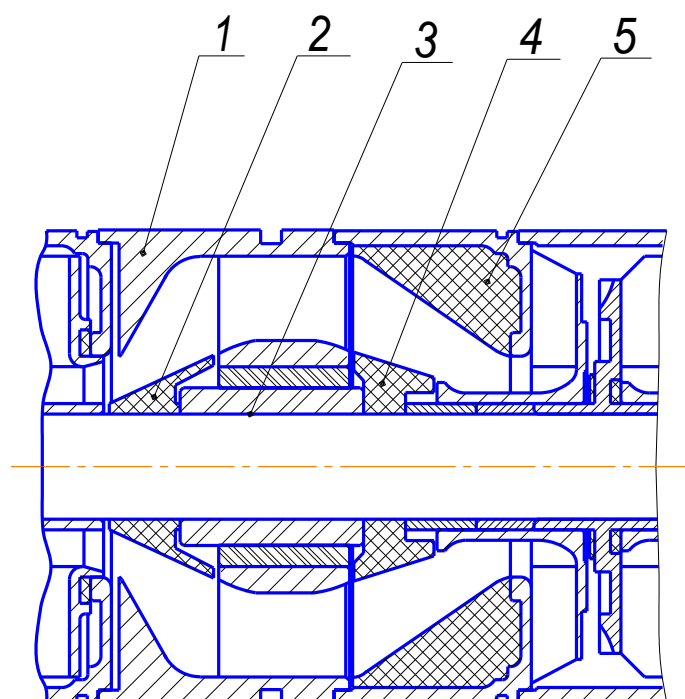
Модернизированная конструкция промежуточного подшипникового узла (1-корпус подшипника; 2-втулка обтекатель; 3-втулка защитная; 4-отбойник; 5-обтекатель направляющего аппарата)
